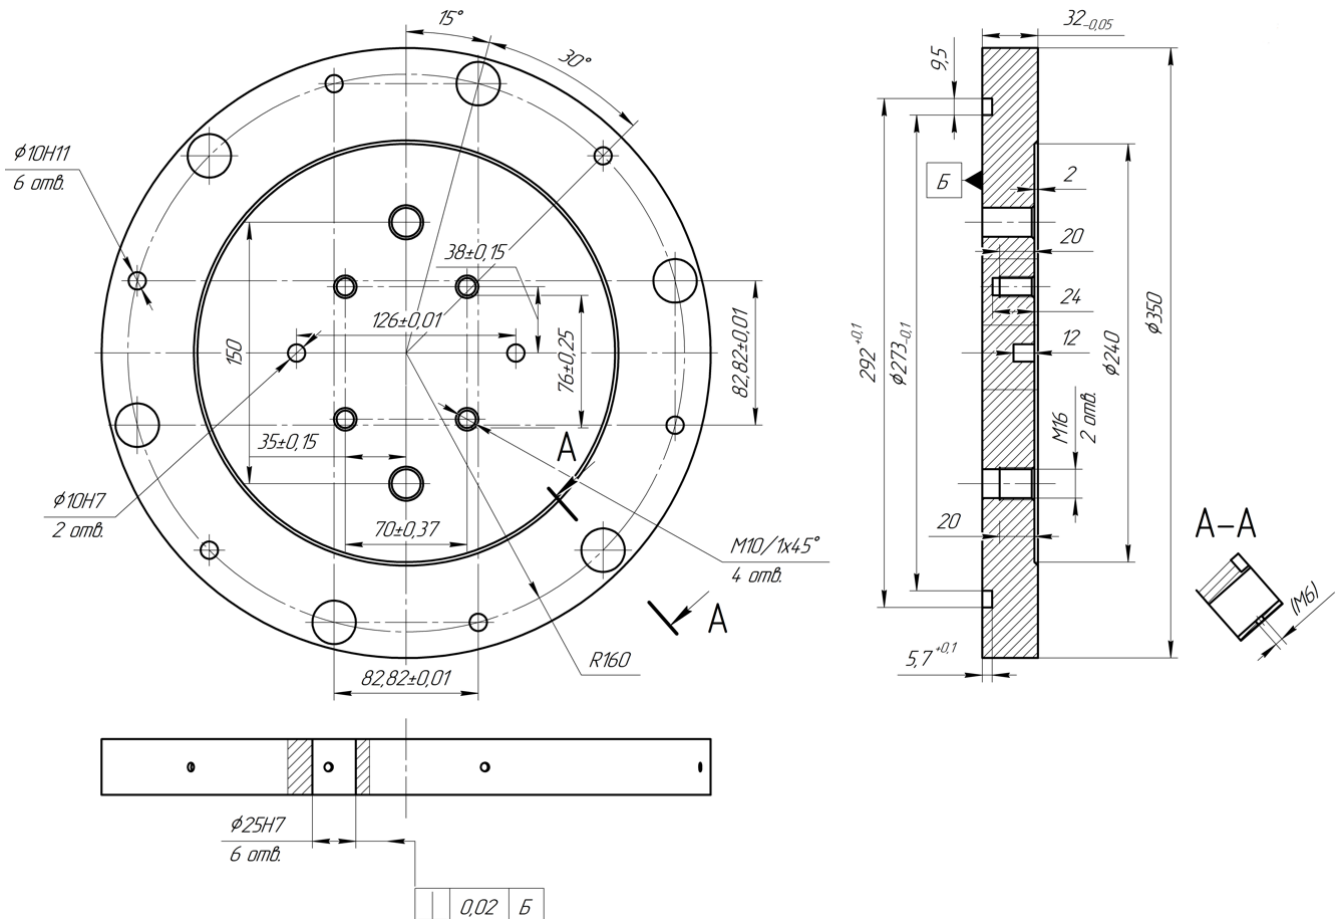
Розмірні зв'язки поверхонь диска
